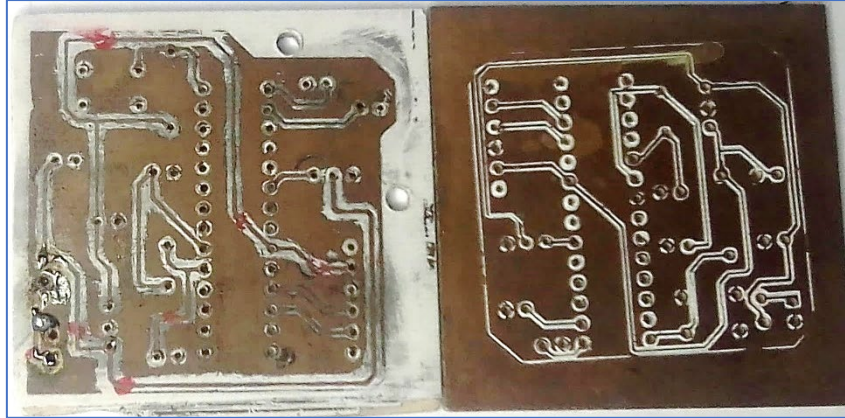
Izquierda) Impresión en placa fenólica y ataque químico; Derecha) Maquinado de placa
